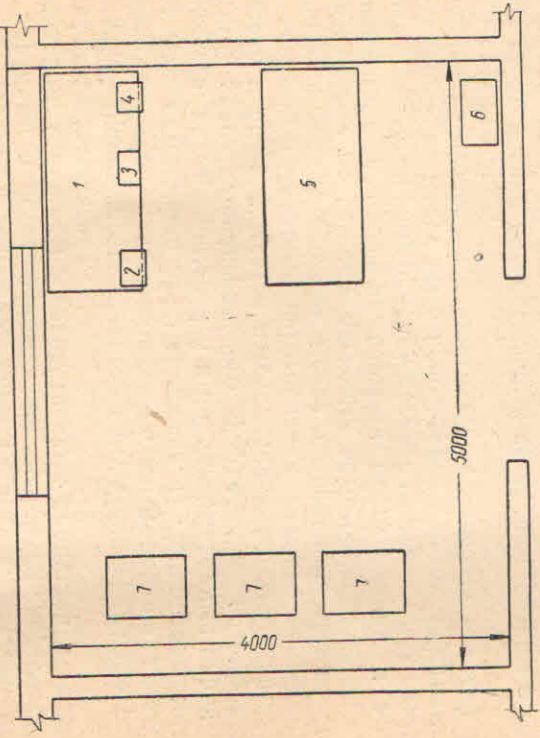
План участка для изготовления автомобильных резиновых деталей:
